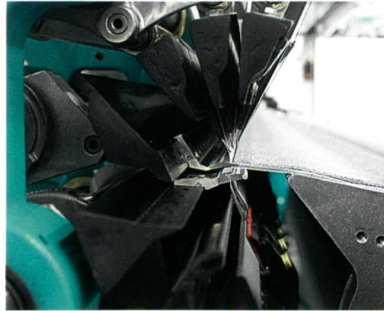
Wirkwerkzeuge der HKS 3-M mit Pol-einrichtung
